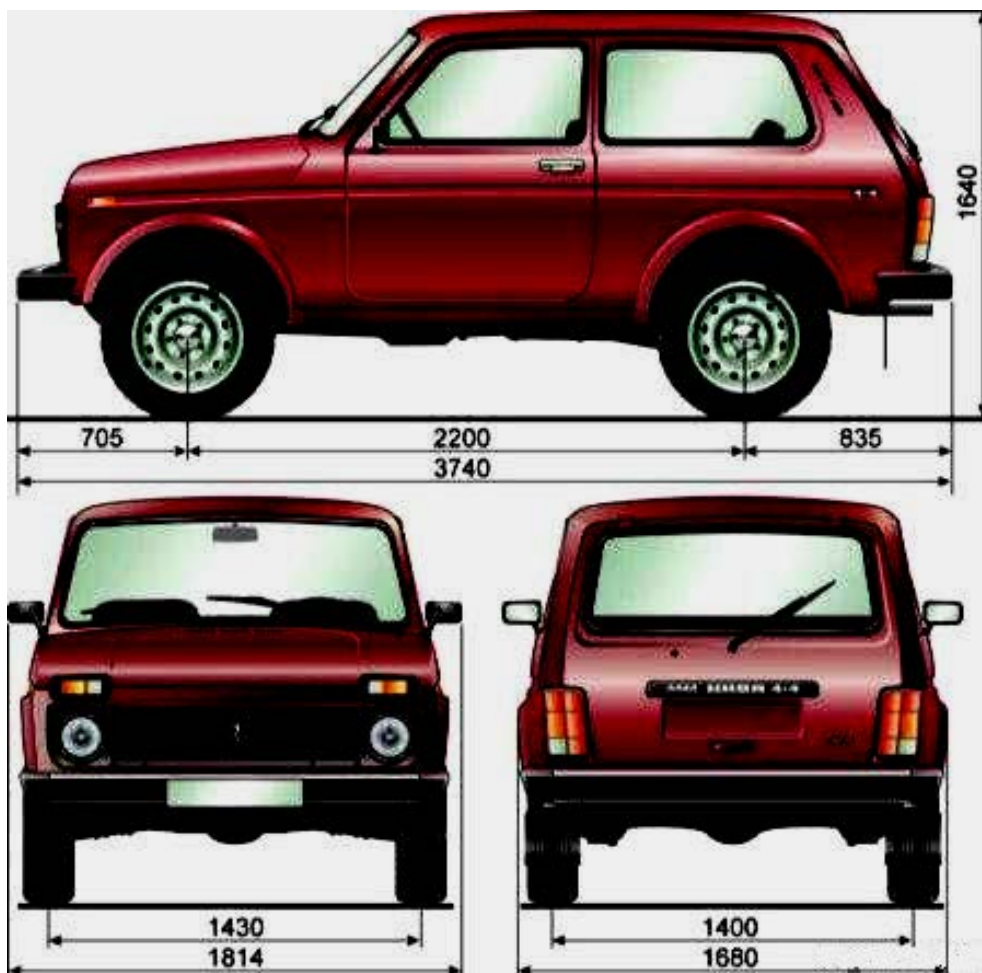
Габаритные размеры автомобиля ВАЗ 2121
